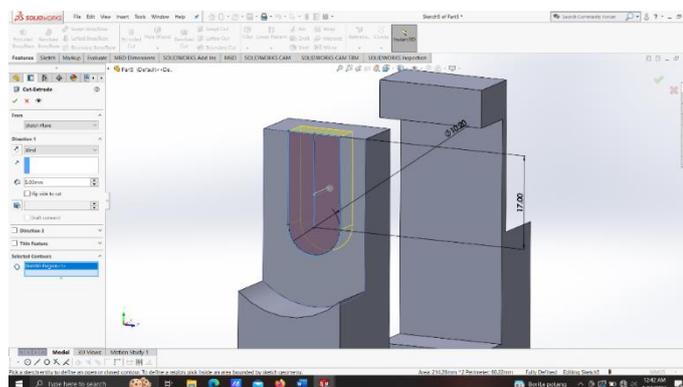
Hasil *Extruded Cut* Dudukan Motor
